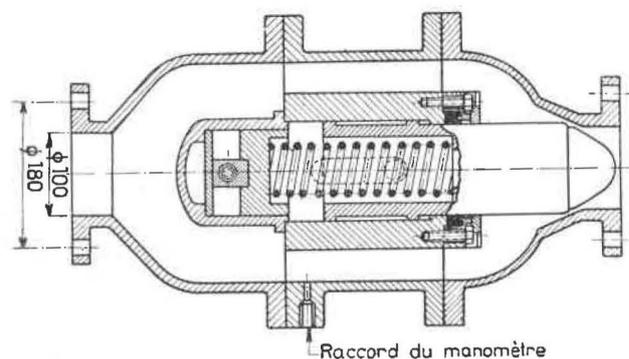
is. — Régulateur d'air automatique « Brieden » pour remblayeuse pneumatique.
